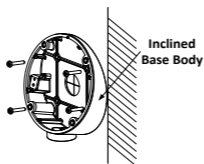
Fixez le boîtier du support incliné au plafond/mur
